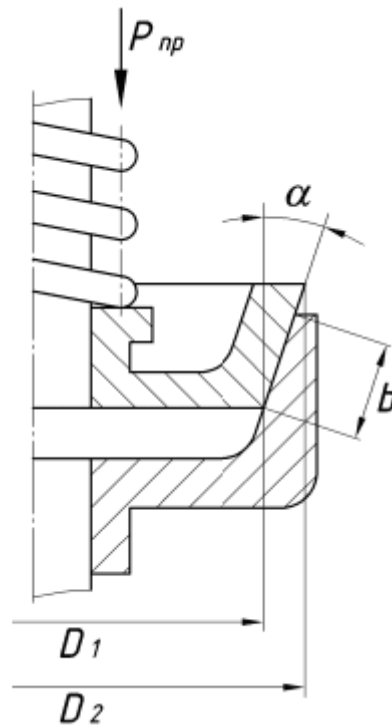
Розрахункова схема для визначення параметрів конусного фрикційно-запобіжного механізму
